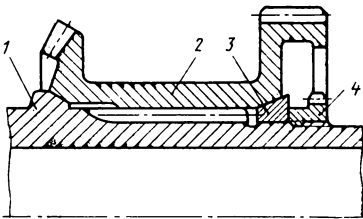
Шлицевое соединение с дополнительными центрирующими поверхностями
